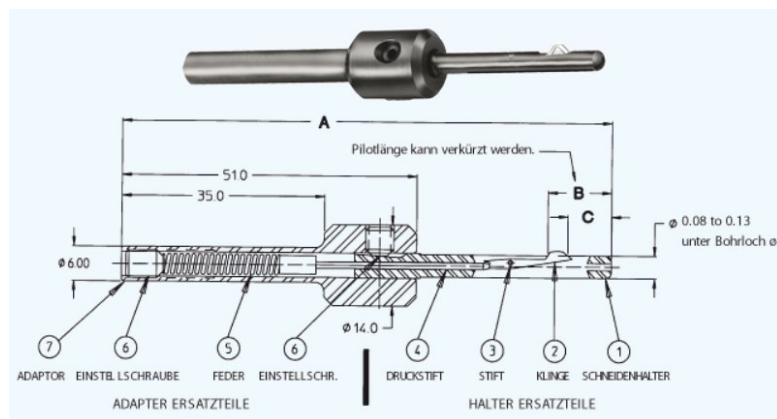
Burraway Entgratwerkzeug Typ MA in Volldarstellung (oben) und aufgeschnitten (unten).¹⁵³
